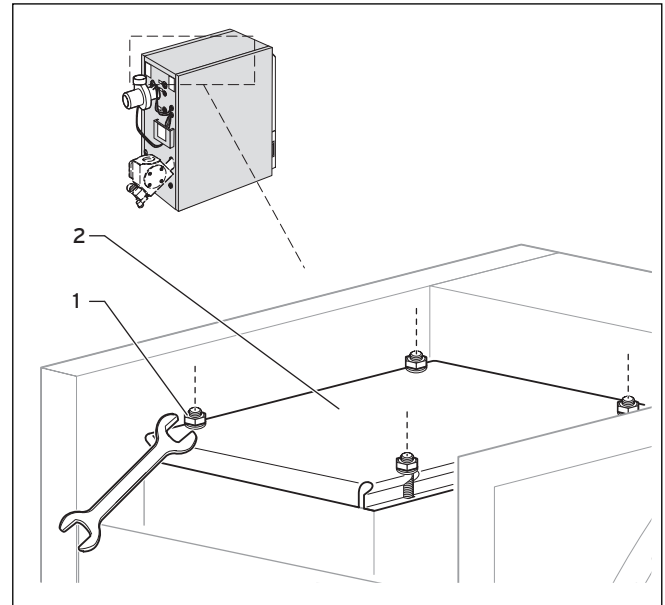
Desatornillar la tapa del intercambiador de calor
